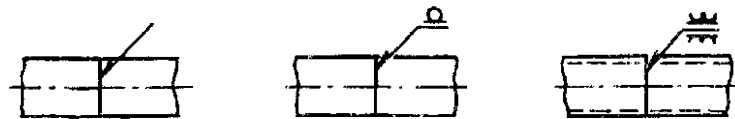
Варианты обозначения швов контактной стыковой сварки
